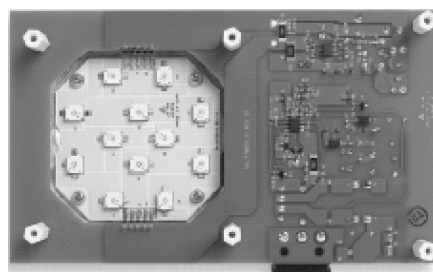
30W LED 驱动电路板 实物图 (PCB 面)
